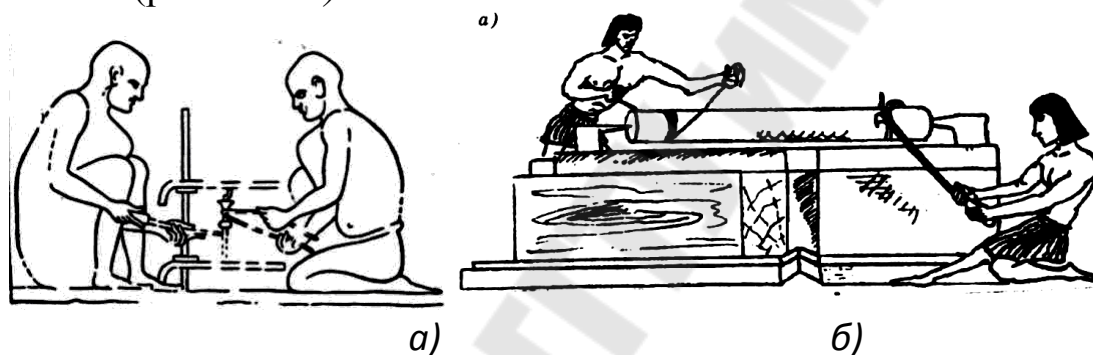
Древнеегипетские токарные станки: *а* – с вертикальным расположением заготовки; *б* – с горизонтальным расположением заготовки
